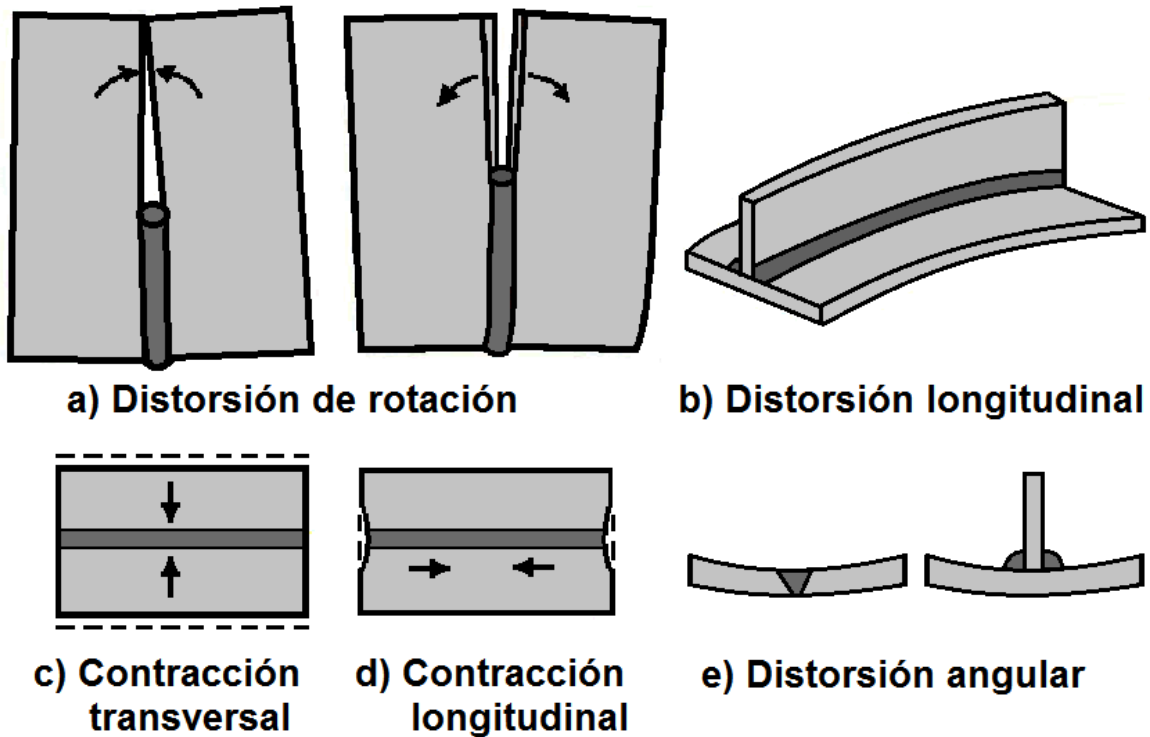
Esquemas de distorsiones en piezas durante la soldadura (8, 18)
